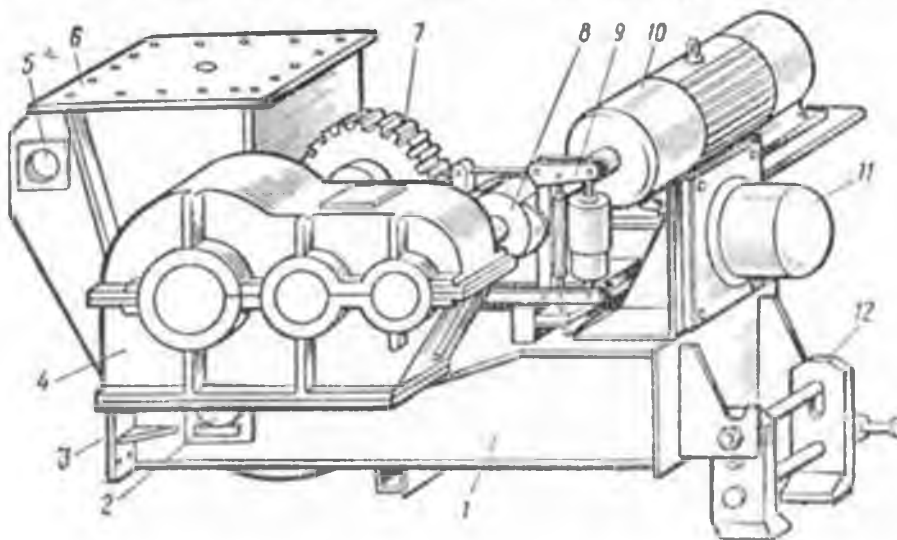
Опорний візок крана КК-5: 1 - рама; 2 - вісь ходового колеса; 3 - фланець опорних стяжок; 4 - редуктор; 5 - цапфа монтажних блоків; 6 - опорна плита; 7 - відкрите зубчасте колесо; 8 - шків; 9 - гальмівний пристрій; 10 - електродвигун; 11 - буфер; 12 - протиугінне захоплення
